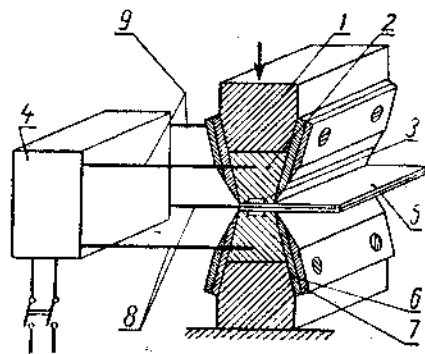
Аппарат для контактно-импульсной сварки:
